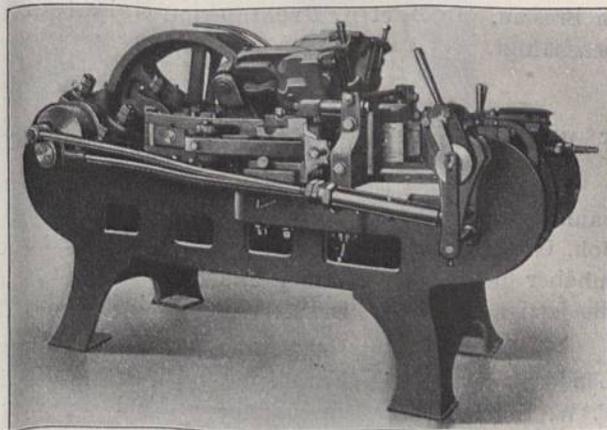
Bolzenschmiedemaschine mit 6 Hämtern.
